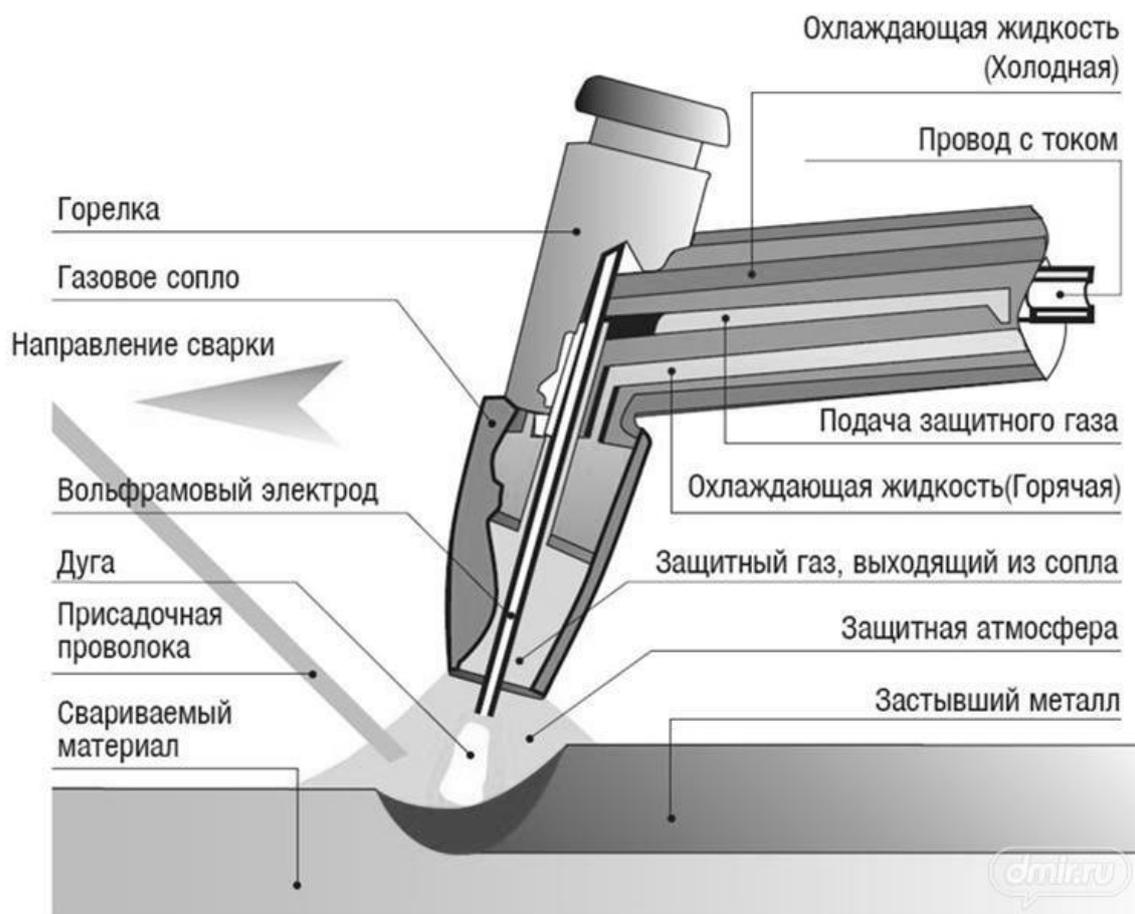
Схема выполнения аргонодуговой сварки
